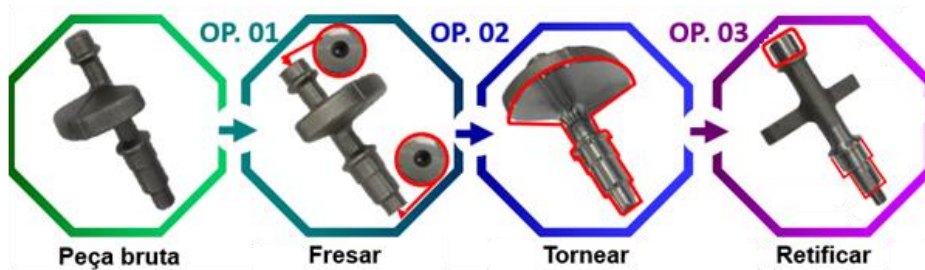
Processo de usinagem de um eixo. Fonte: Autores, (2023).
